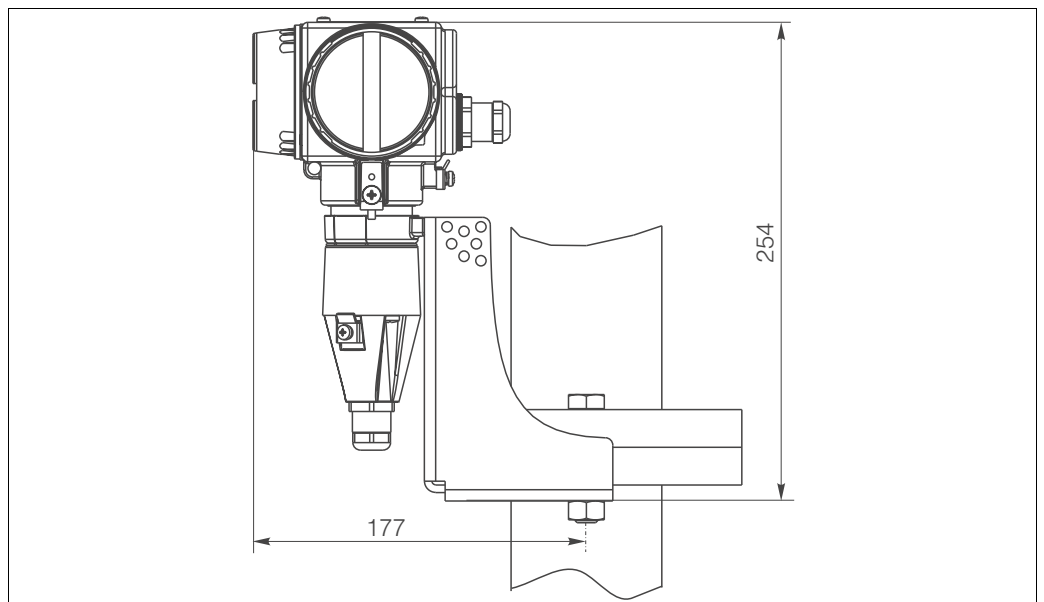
MyPro: Flanschmontage m. Befestigungswinkel (bei CXM431-xxx4xx im Lieferumfang)
